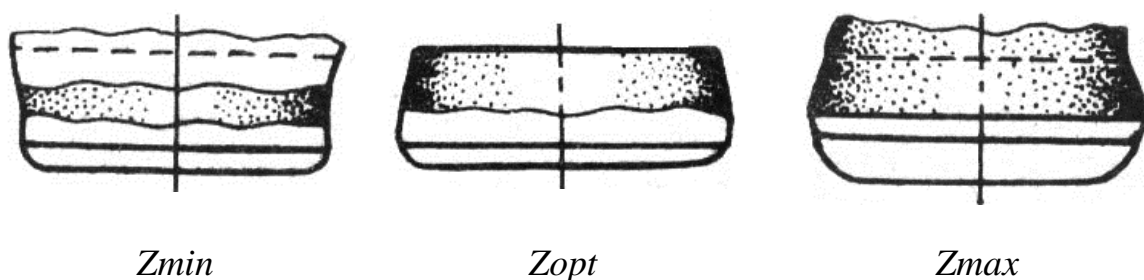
Зовнішній вигляд поверхні зрізу при різних зазорах
